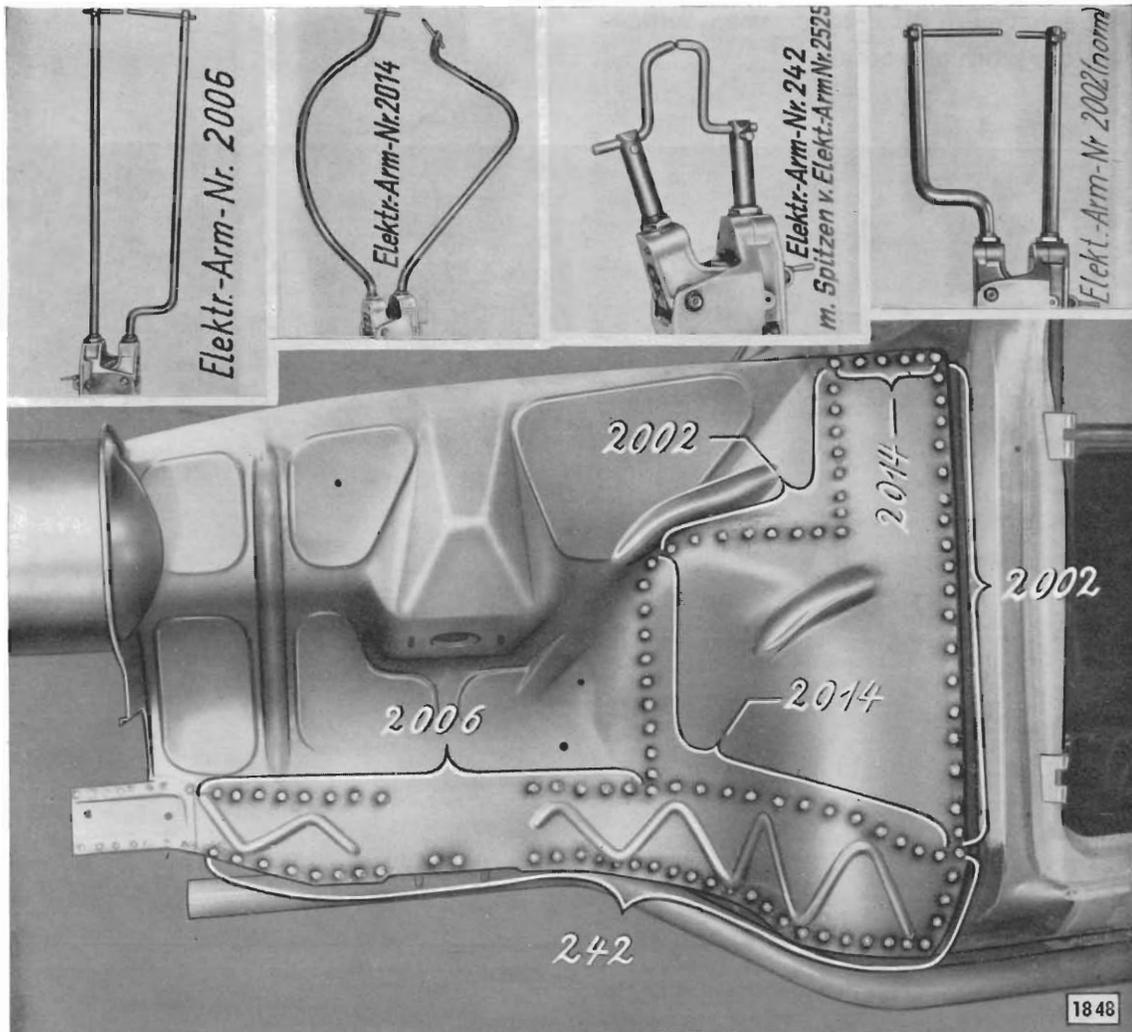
Linken Radeinbau an Längsträger, Stirnwand, Karosserie-Scharniersäule und senkrechten Flansch der Einstiegverkleidung punktschweißt – rechten Radeinbau in gleicher Weise punktschweißen
